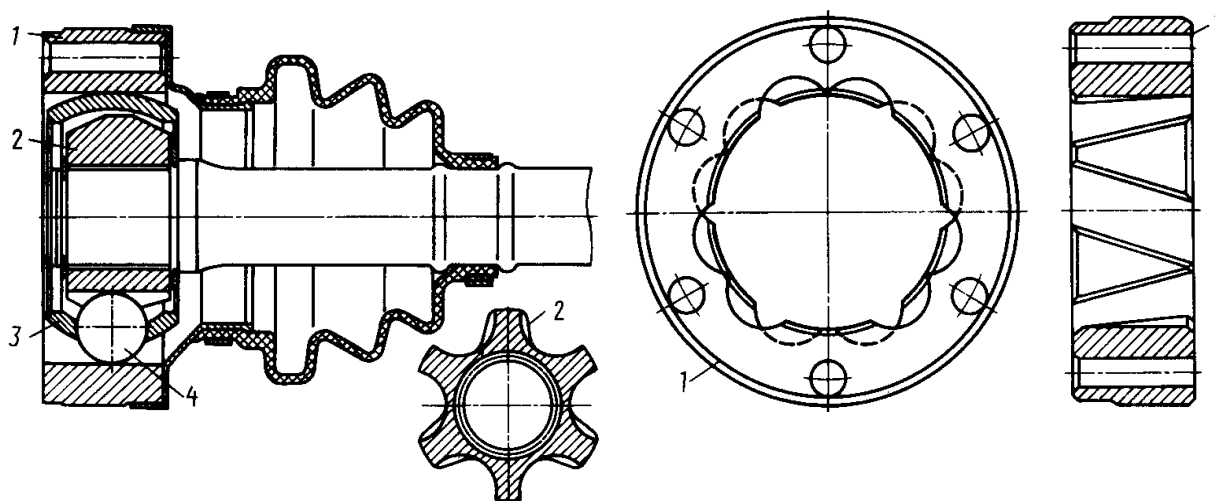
Шестишариковый универсальный карданный шарнир типа “Лебро”
